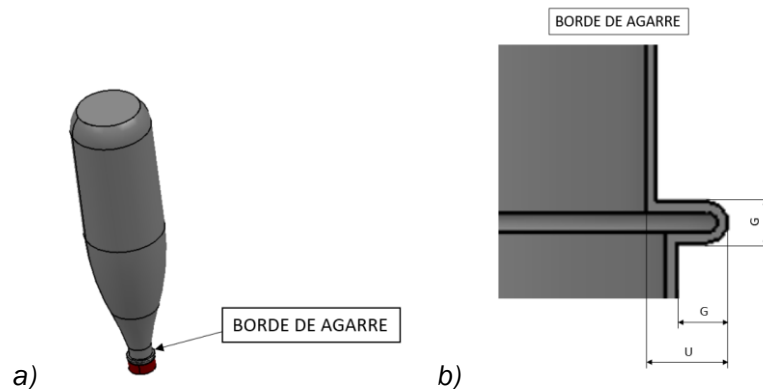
a) Vista isométrica de la botella usada como cohete; b) Dimensiones del borde de agarre.
